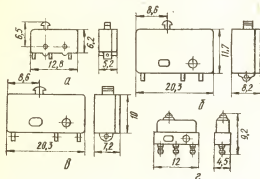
Габаритные чертежи микропереключателя типа МП:
